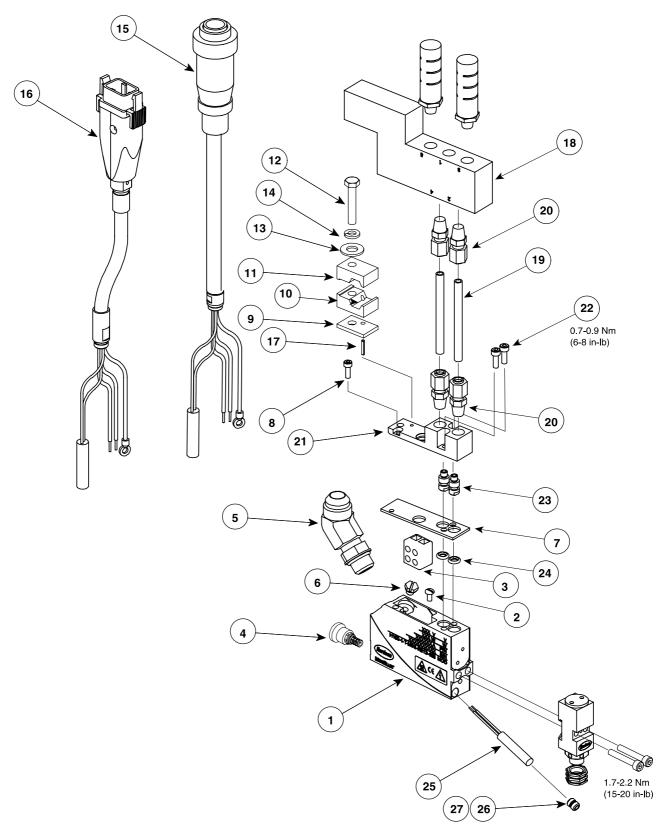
Pistolet mono-module ultra-plat à électrovanne SG
